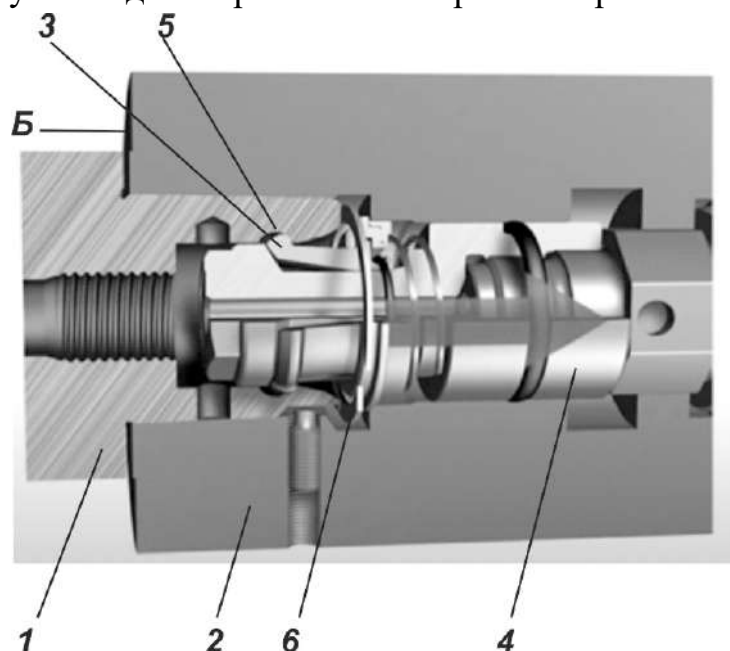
Схема закріплення інструментальної оправки Coromant Capto
